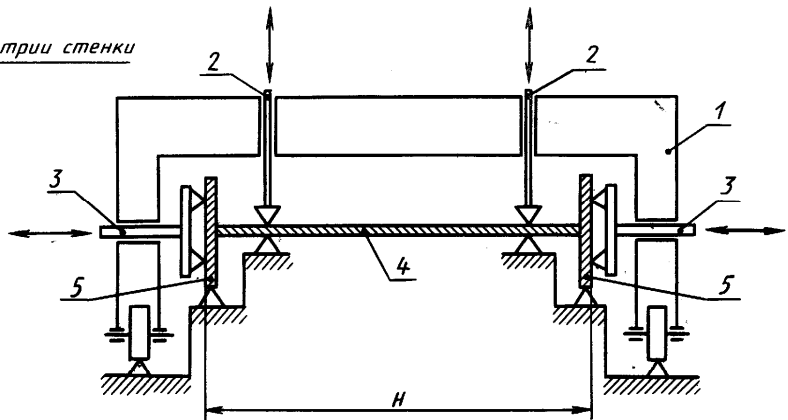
Схема самоходного портала для сборки двутавровых балок
